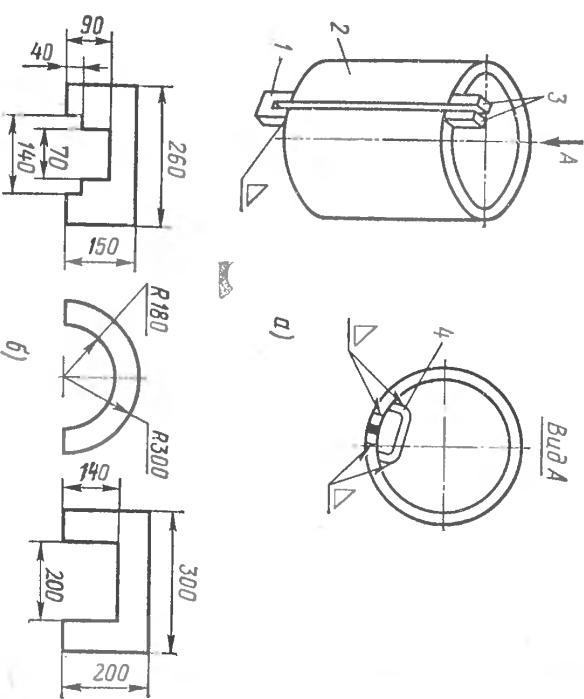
Подготовленная к электрошлаковой сварке заготовка в сборе (а) и виды скоб (б):
